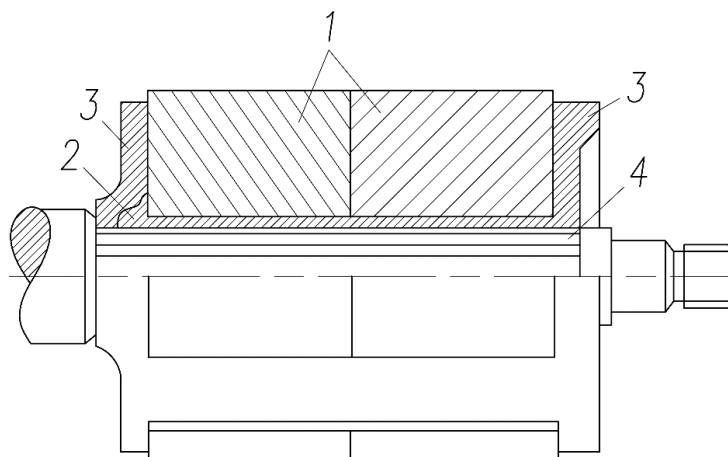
Конструкция ротора с постоянными магнитами: 1 — магниты; 2 — втулка; 3 — заливка из алюминия; 4 — вал.
